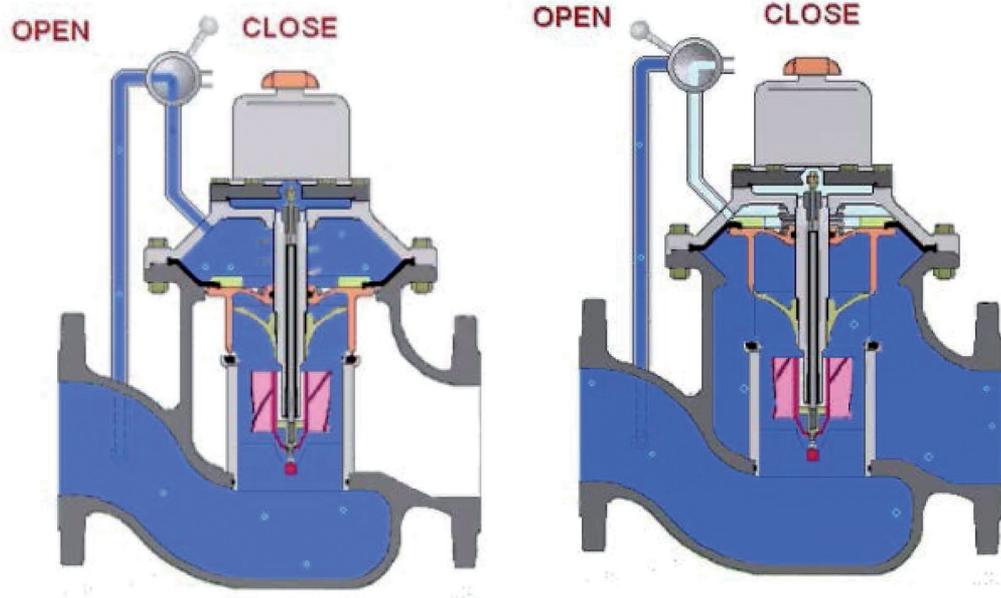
válvula contador seccionada cerrada y abierta. Fuente Bermad.
